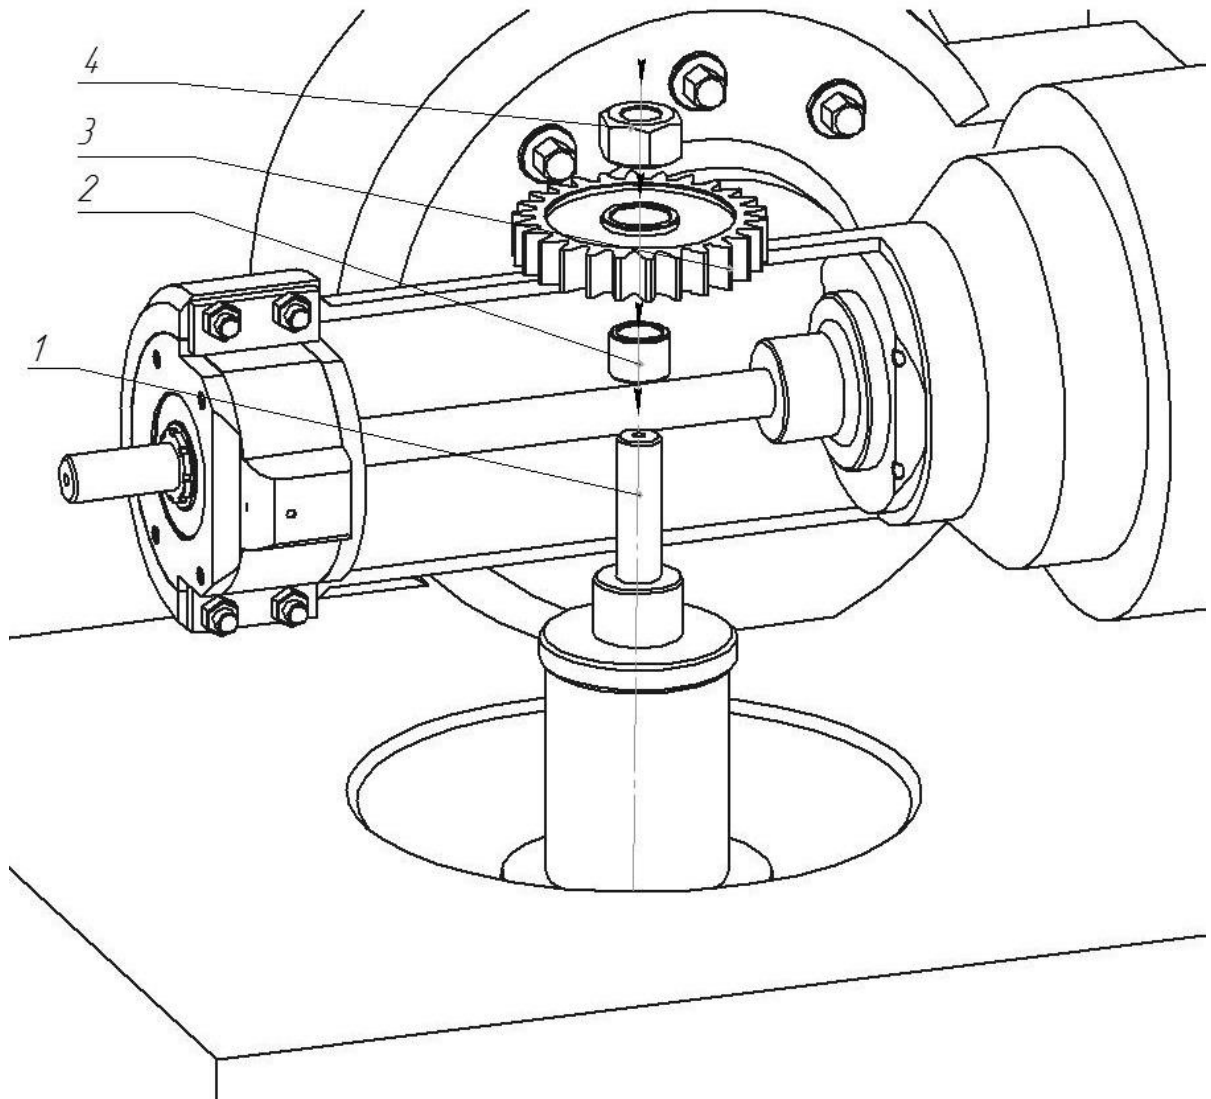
Встановлення циліндричного зубчастого колеса на
